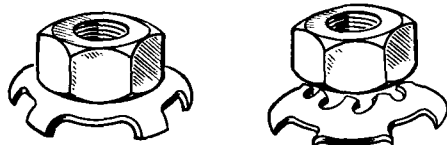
Стопорение гайки выпуклой хриповой шайбой с наружными зубцами
